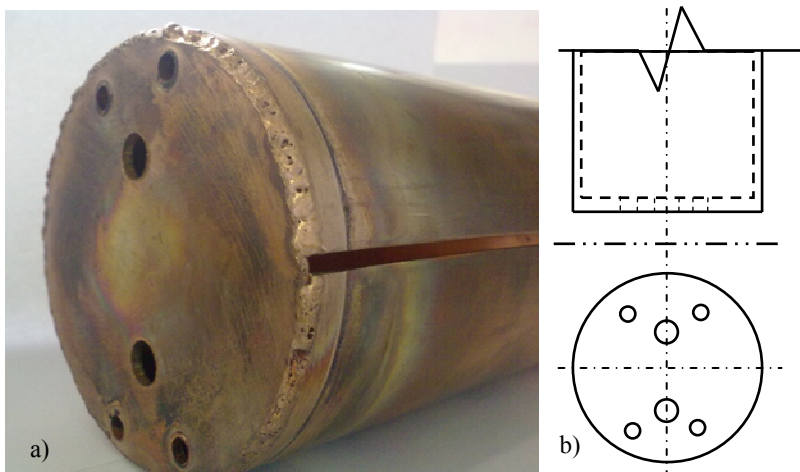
Montagem da proteção (guard heater) a) Imagem b) Desenho.
